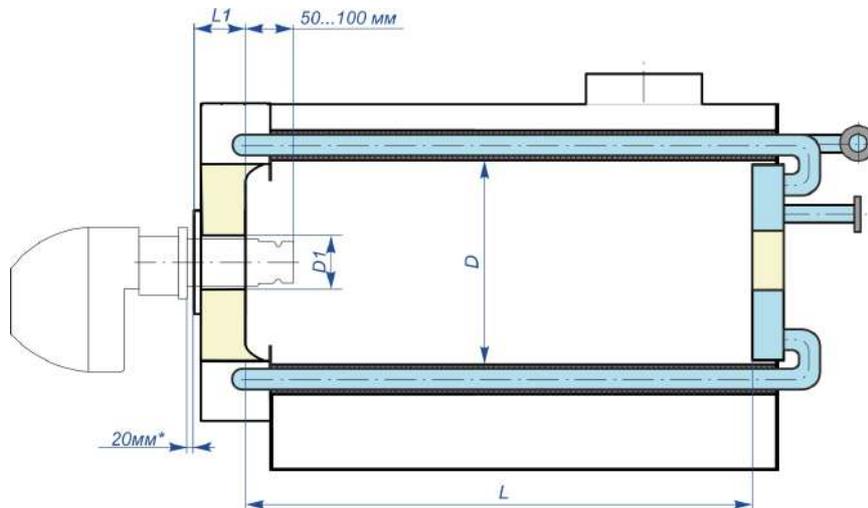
Габаритные и присоединительные размеры котлов RSD13000 – RSD20000
